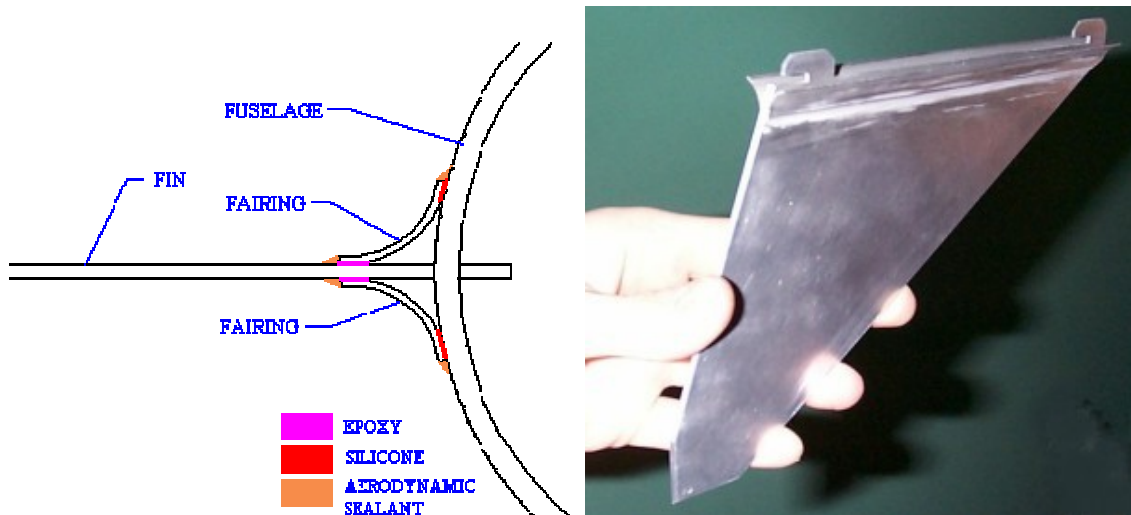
Aletas del Cirrus Uno: Izd.: Fijación, vista desde arriba. Dch: Ensamblaje
